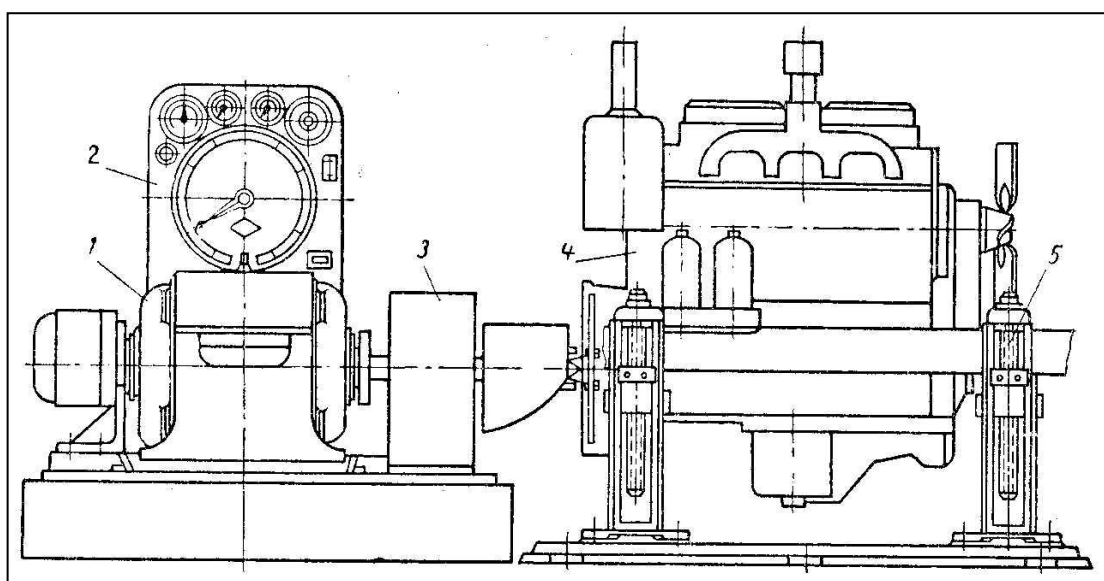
Схема расположения малогабаритных стендов для обкатки автомобильных двигателей
